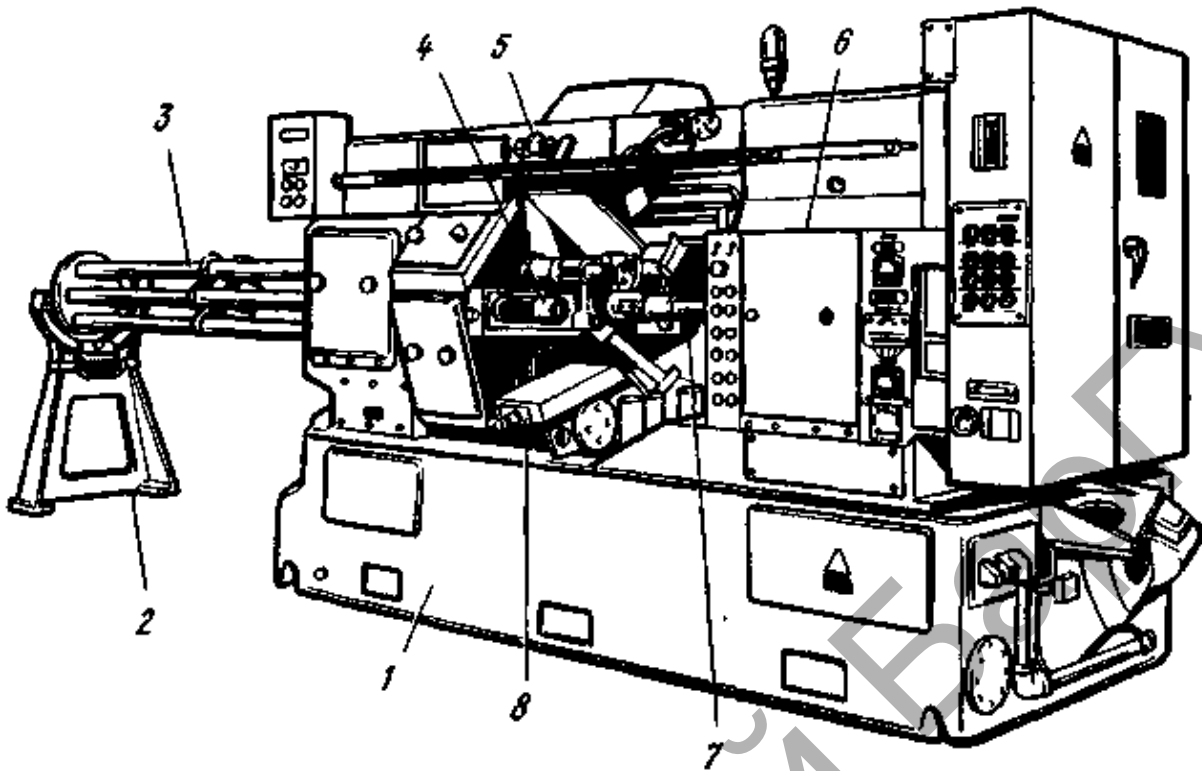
Общий вид шестишпиндельного токарного автомата
